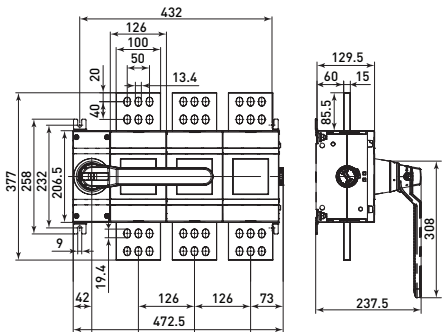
Габаритные и установочные размеры рубильников 2000-2500 А 3Р
